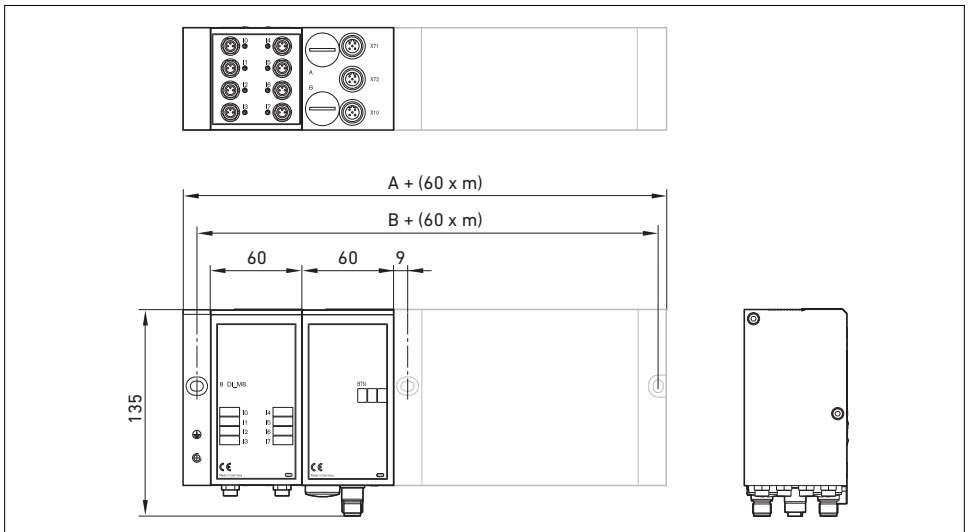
Disegno quotato del sistema di valvole (accoppiatore bus e valvole)
